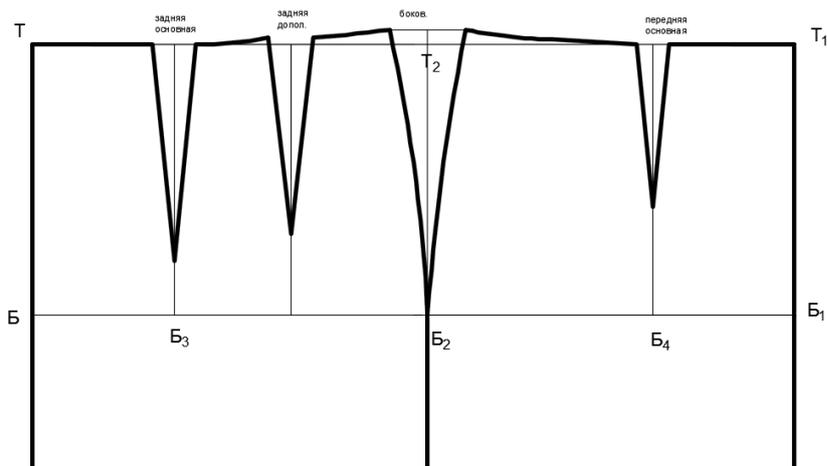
Схема чертежа конструкции юбки с двумя вытачками сзади (фигура с выступающими ягодицами)
